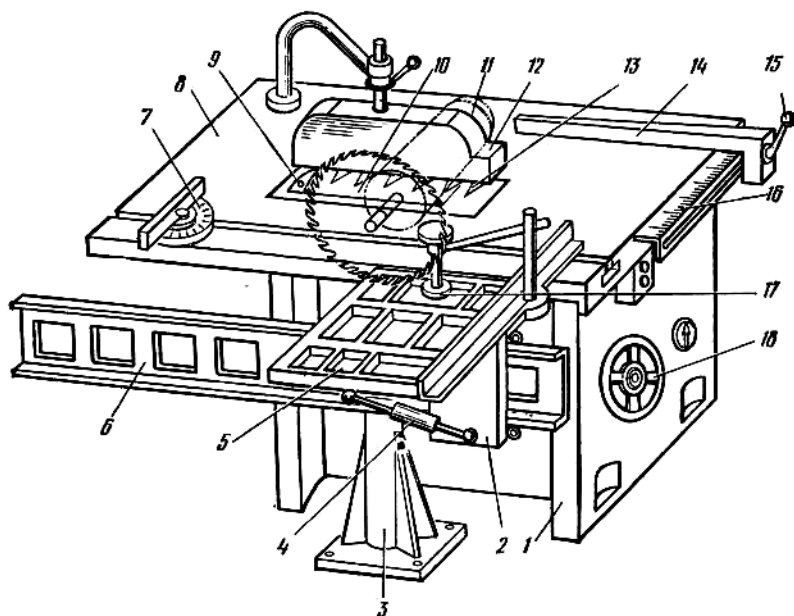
Универсальный круглопильный станок для смешанной распиловки Ц6-2:
